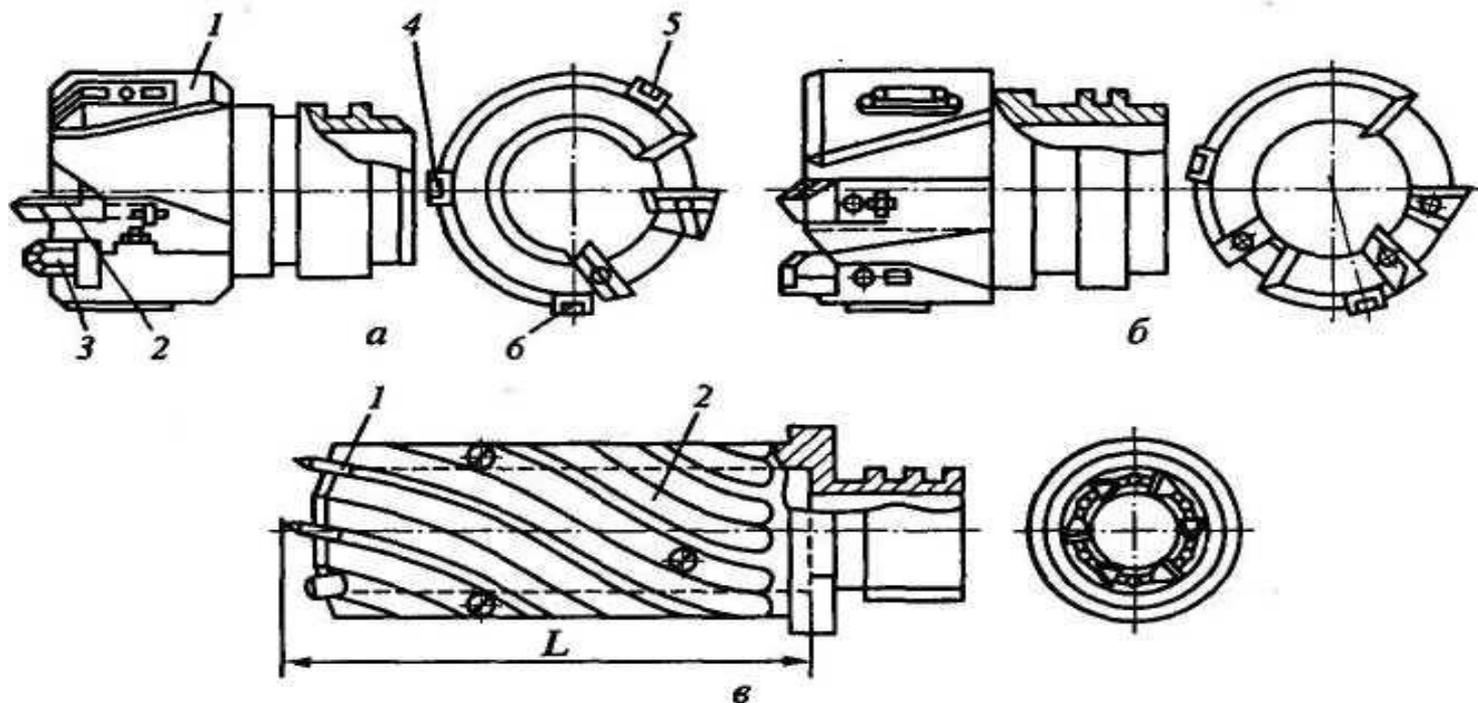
Кольцевые сверла: а - двурезцовые: 1 - корпус; 2,3- сменные резцы; 4,5,6- направляющие пластины; б - трехрезцовые; в - многорезцовые: 1 - резцы; 2 - корпус; L - длина рабочей части
